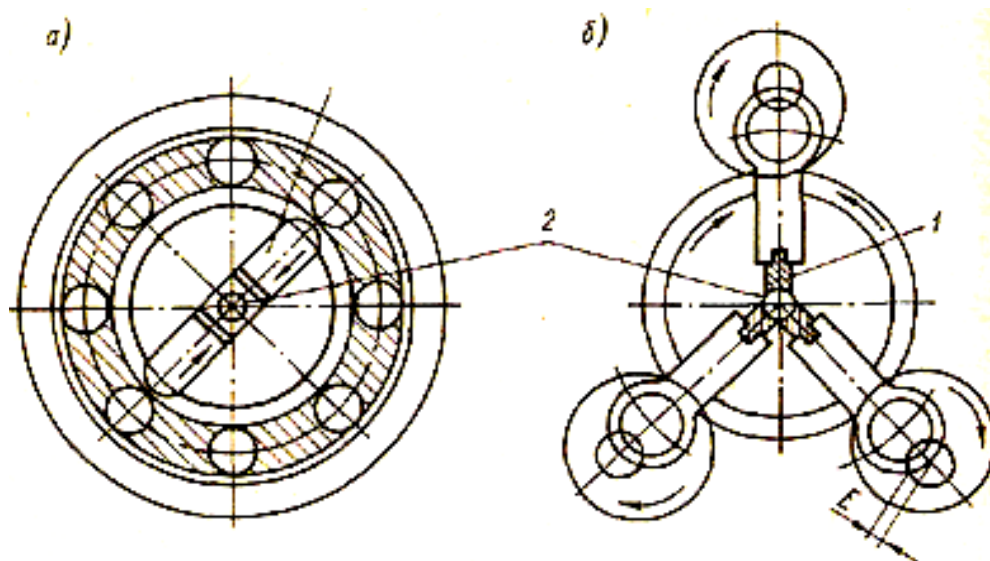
Схема ковки на ротационно-ковочной (а) и радиально-обжимной (б) машинах: 1-бойки, 2-заготовка, Е-ход бойков.
